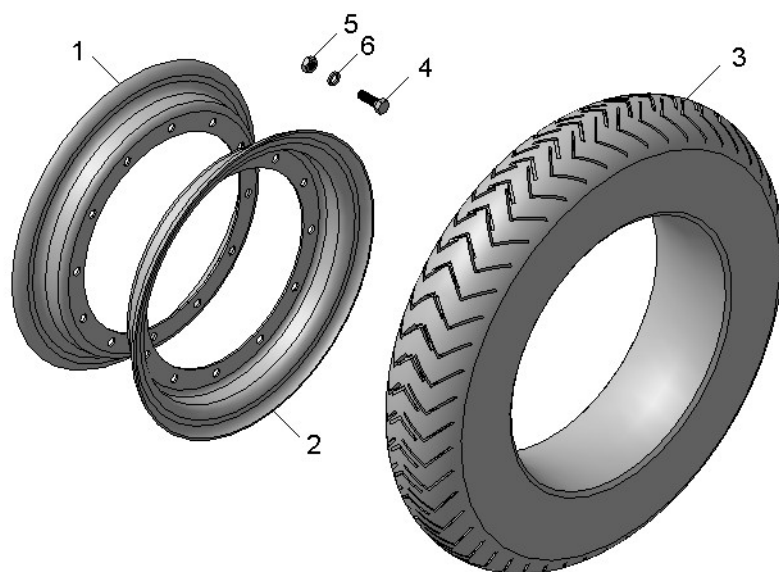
Колесо с камерой и покрышкой в сборе 8122-3107010
